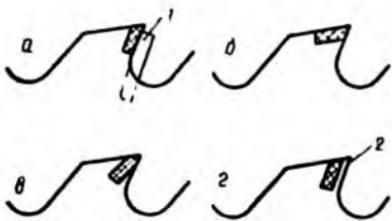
Варианты расположения пластинок из твердого сплава в пазу резца:
